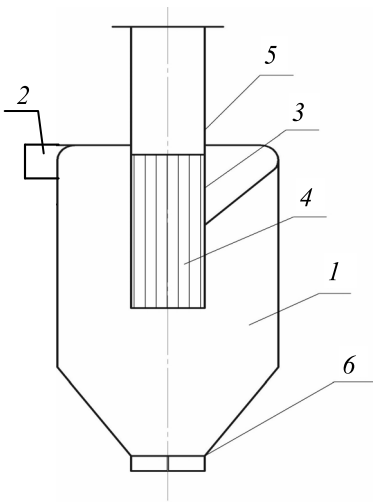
Пилувловлювач: 1 – циліндрично-конічний корпус пилувловлювача; 2 – тангенційний вхідний патрубок; 3 – жалюзійний відокремлювач; 4 – жалюзі; 5 – вихлопний патрубок; 6 – пиловипускний патрубок.
